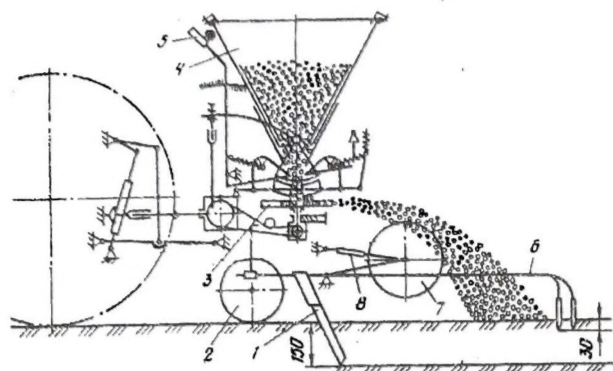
Технологическая схема комбинированного агрегата: 1-щелерез; 2-опорное колесо; 3-разбрасывающий диск; 4-бункер; 5- рычаг для регулировки нормы высева удобрений; 6- зубовые борона; 7-транспортное колесо; 8-гидроцилиндр
